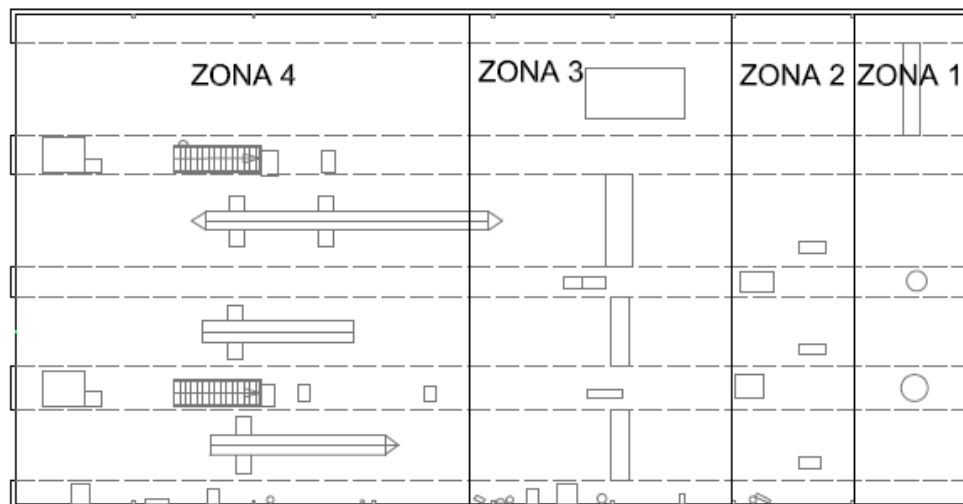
Planta de la nave con zonas delimitadas donde se lleva a cabo cada operación.
